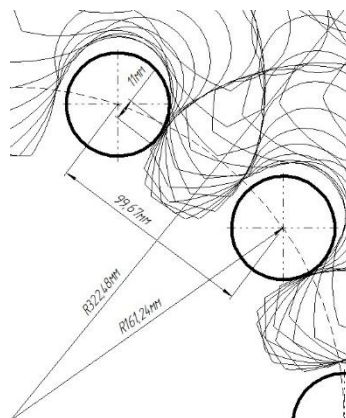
Кинограмма работы кинематической пары зубчатое колесо – цевочный барабан
